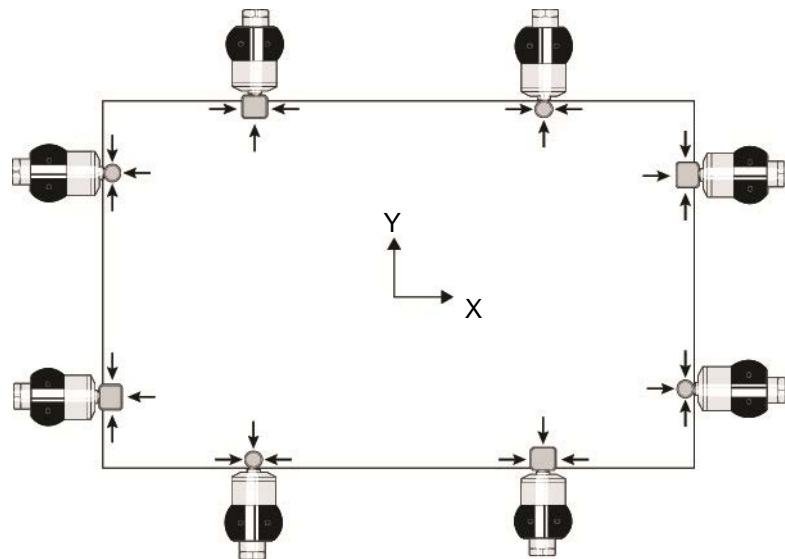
Beispiel für Bewegungen von Werkzeugmaschinen
